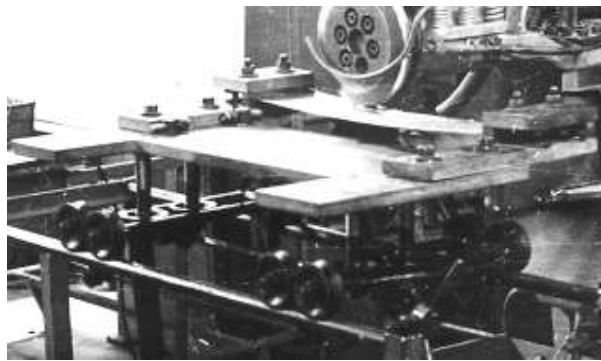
Внешний вид установки для формирования листовых металлокомпозитов
